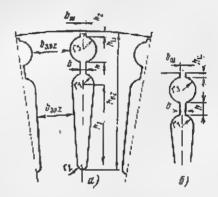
Форма паза ротора двигателя с двойной клеткой.
